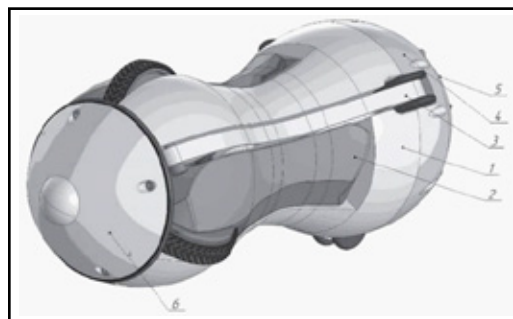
корпус МК (механической конструкции); 2 – нога приводная опорная с колесным движителем; 3 – нога неприводная опорная с колесным движителем; 4 – отсек корпуса МК; 5 – задняя крышка; 6 – передняя крышка. Изображение: пресс-служба ПНИПУ
